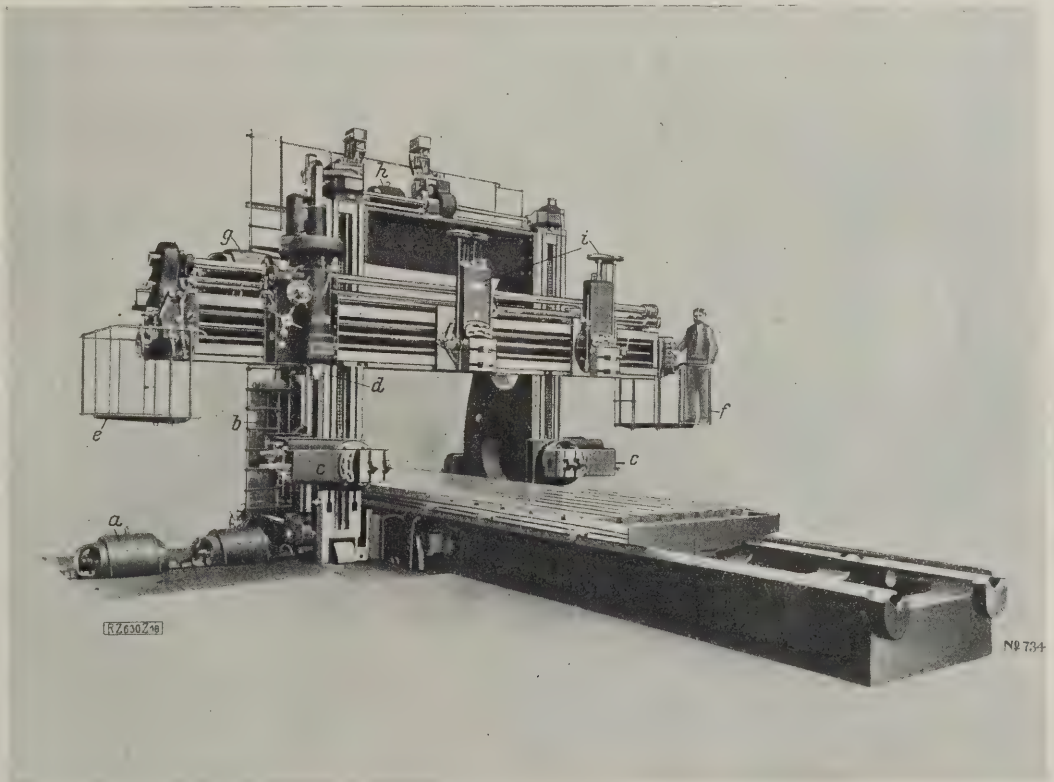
Hobel- und Fräsmaschine der Maschinenfabrik Froriep, Rheydt.
